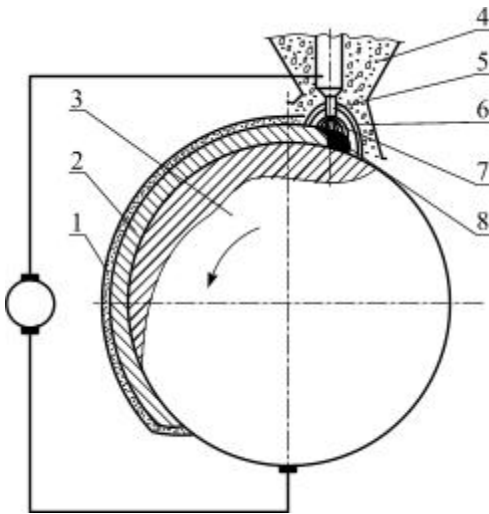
Схема наплавлення під шаром флюсу: 1 – шлакова кірка; 2 – наплавлений шар; 3 – деталь; 4 – флюс; 5 – електродний дріт; 6 – еластична оболонка; 7 – електрична дуга; 8 – ванночка з розплавленим металом
